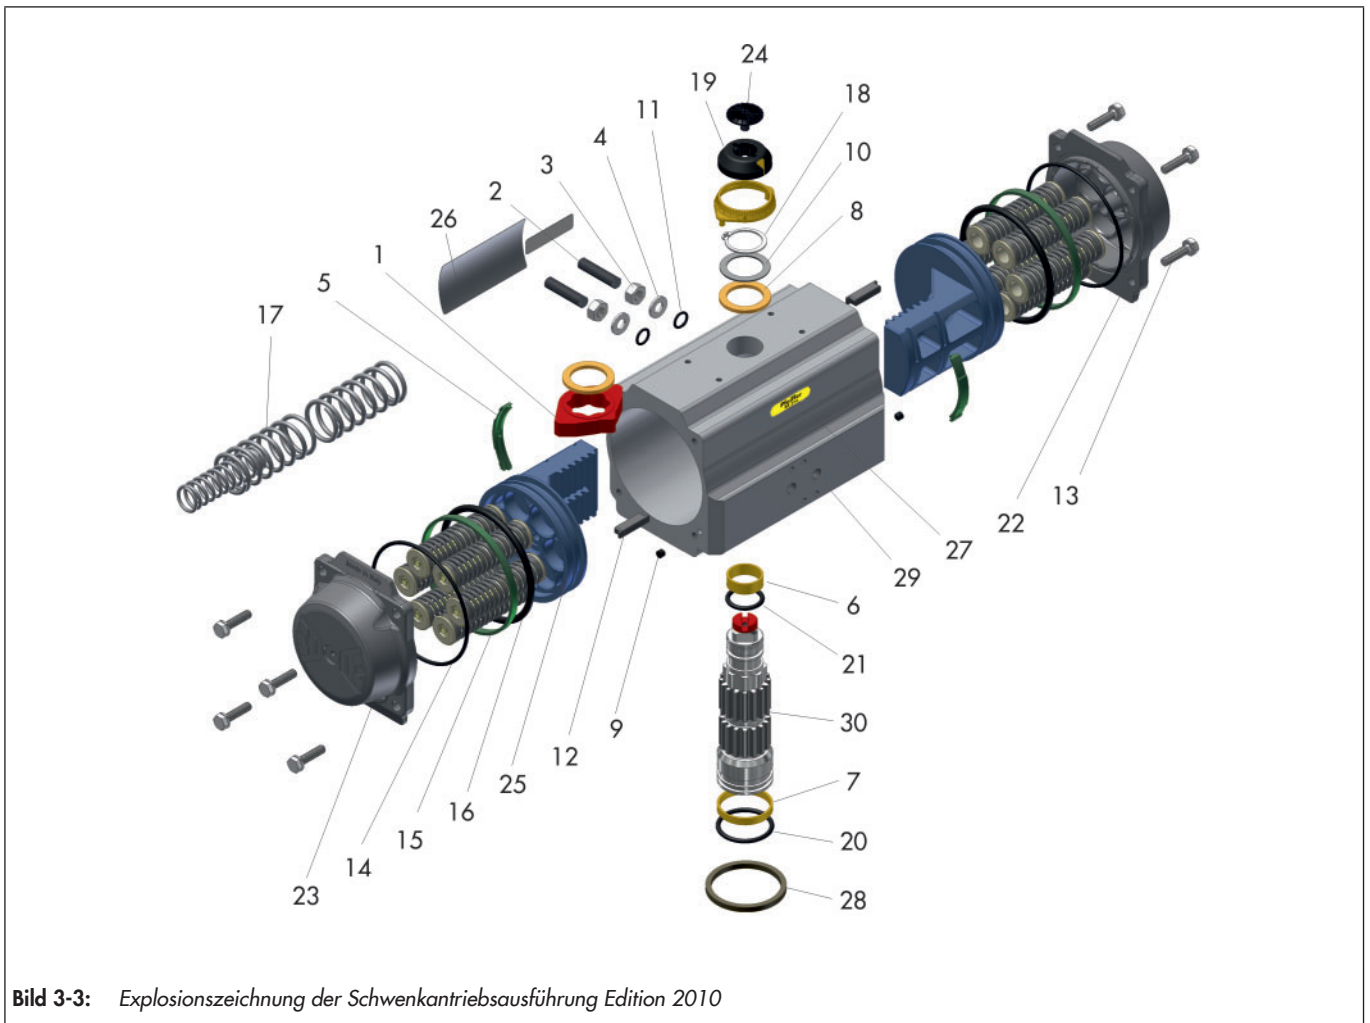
Explosionszeichnung der Schwenkantriebsausführung Edition 2010
